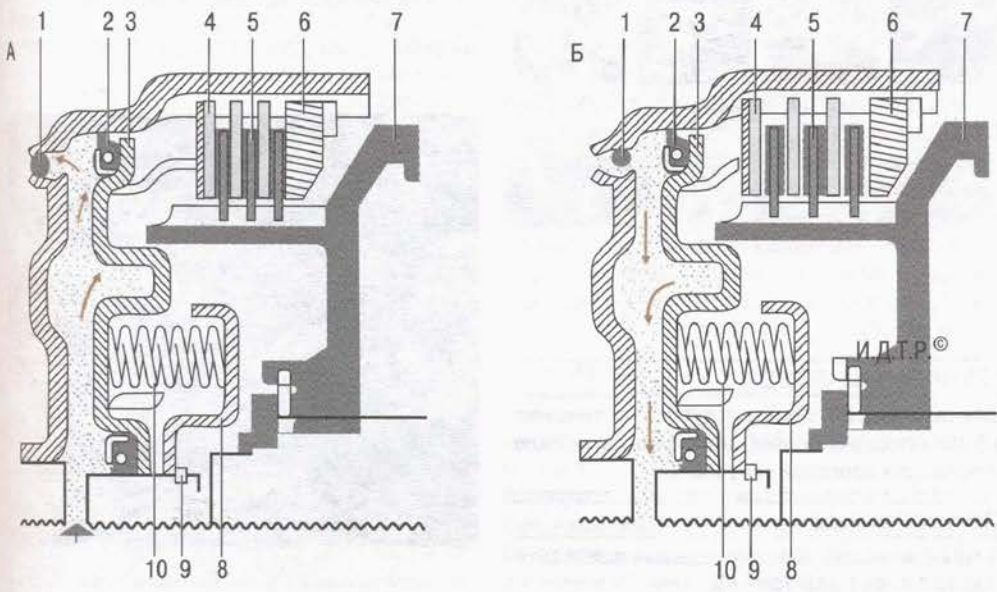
Схема работы многодисковой муфты: А – многодисковая муфта включена; Б – многодисковая муфта выключена; 1 – шариковый клапан; 2 – уплотнительное кольцо; 3 – поршень; 4 – фрикционный диск; 5 – фрикционный диск с накладками; 6 – упорный диск; 7 – ступица муфты; 8 – упор пружины; 9 – стопорное кольцо; 10 – возвратная пружина
